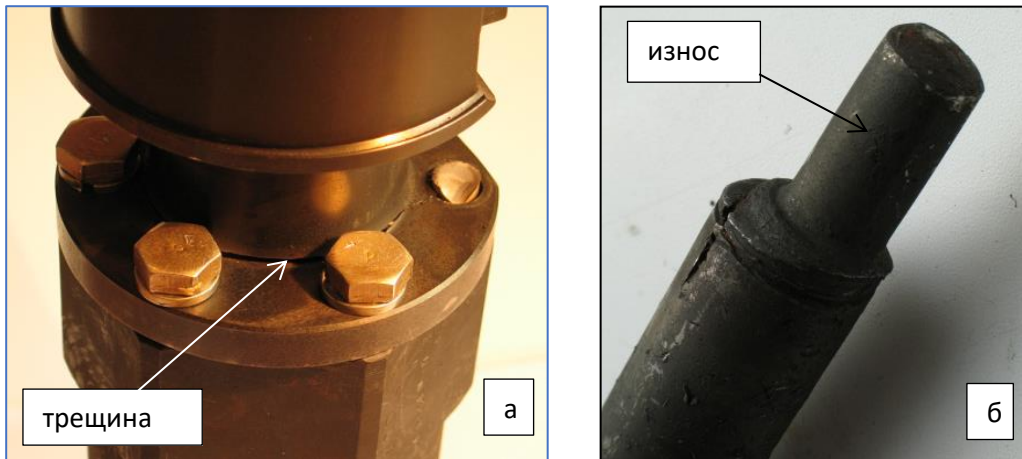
Разрушение корпусных деталей (а) и валов (б)
